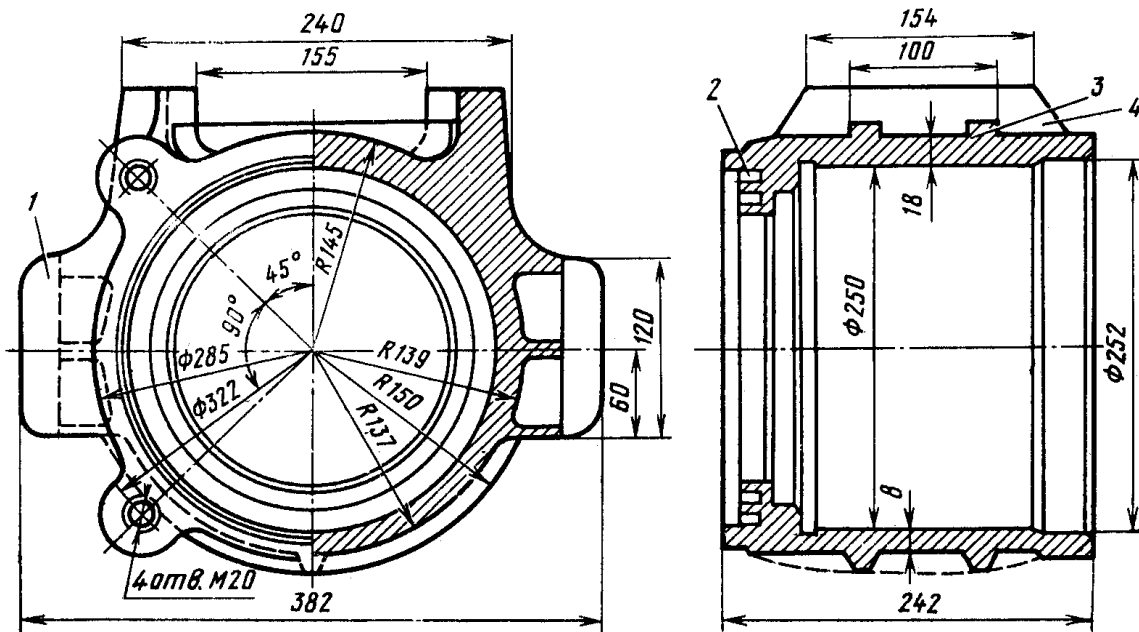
Стальний корпус букси вантажного вагона
